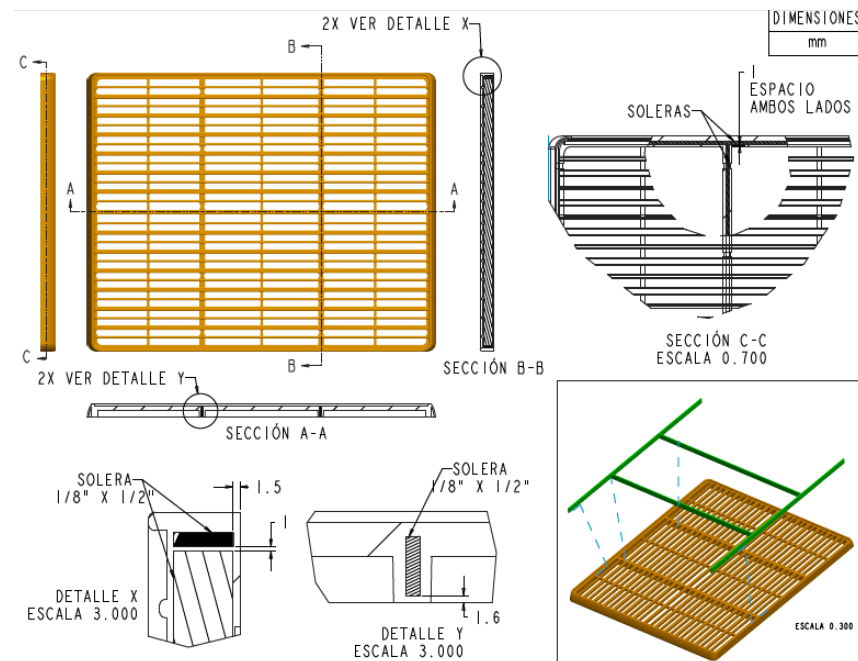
Parrilla híbrida “plástica-metálica” refuerzos en H
